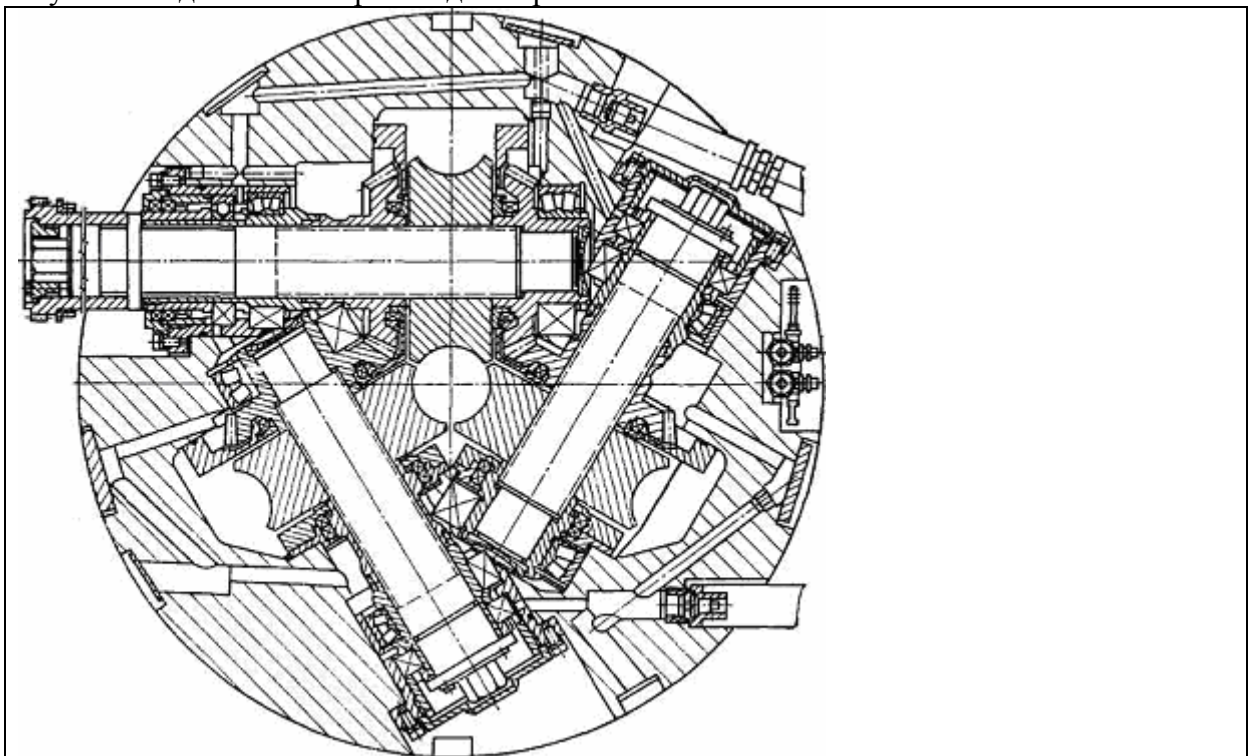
Конструкция трехвалкового рабочего блока с внешним приводом одного валка и внутренним приводом двух других валков коническими шестернями
